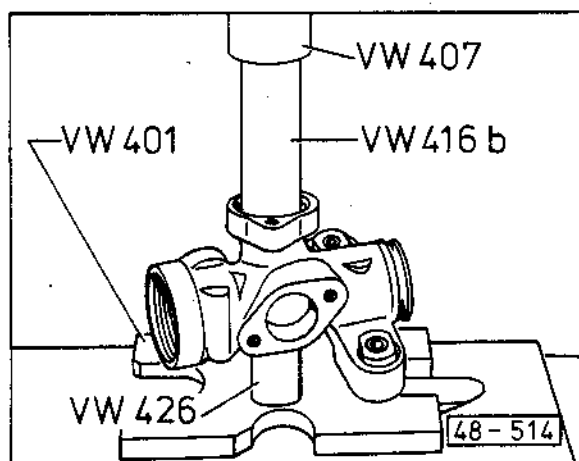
Dichtring in Ritzelgehäuse eindrücken
